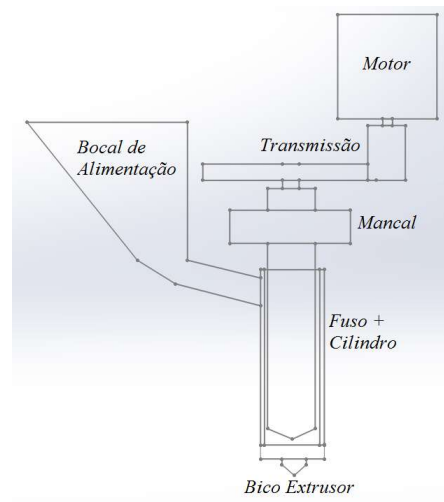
Concepção do cabeçote extrusor a ser acoplado à impressora 3D
